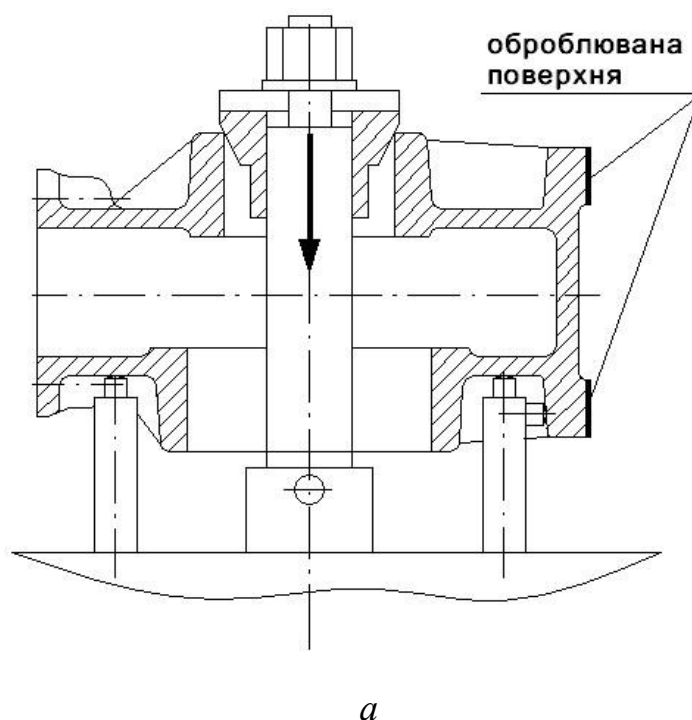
Схеми пристосувань для обробки корпуса (початок)
